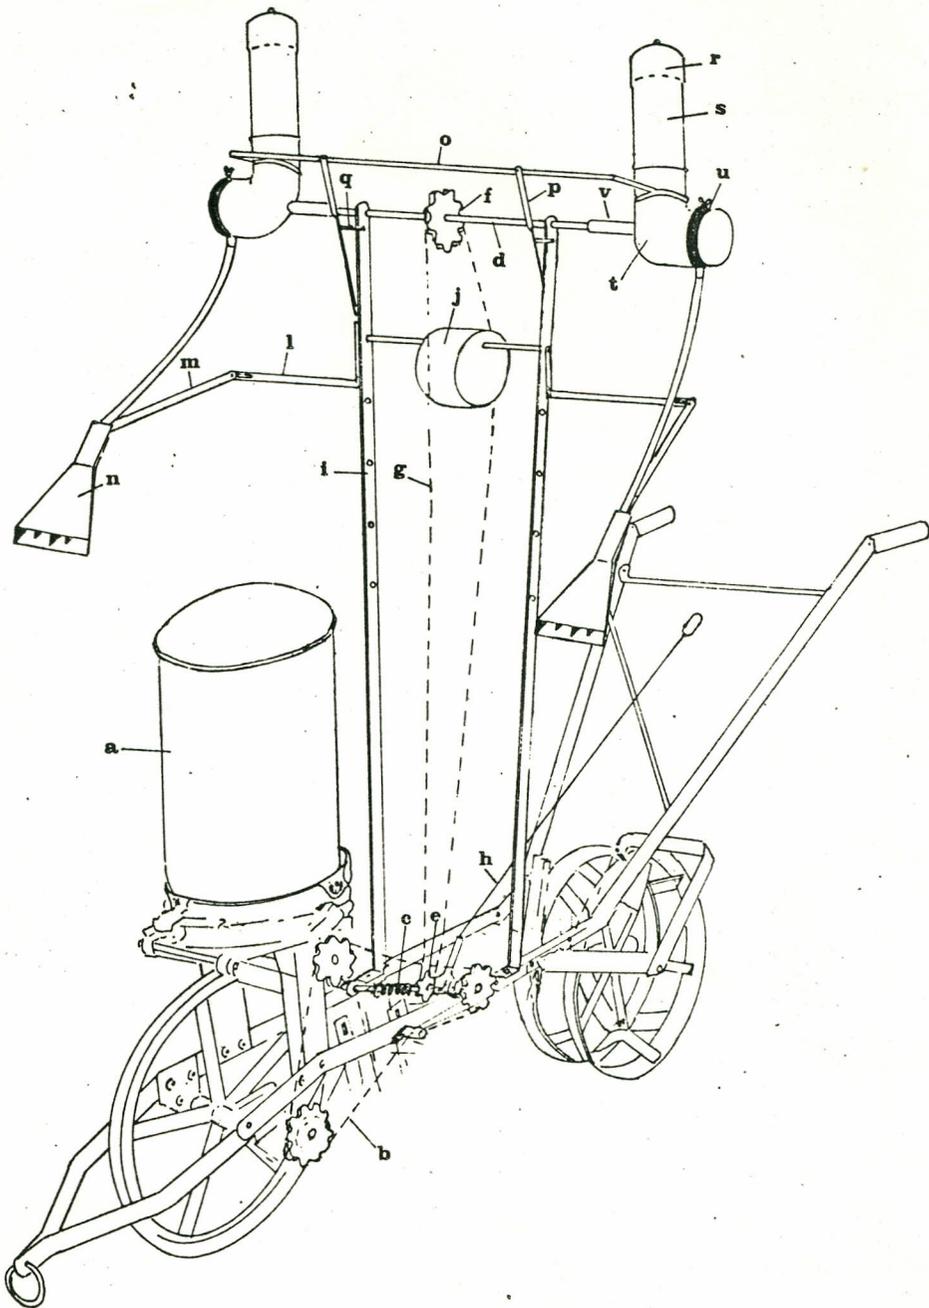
Desenho esquemático do implemento para aplicação de inseticida granulado diretamente no cartucho das plantas de milho ou de sorgo, adaptado à plantadeira de tração animal. (a) - Depósito de adubo; (b-g) - corrente; (c-d) - eixo; (e-f) - engrenagem; (h) - alavanca para acionar o sistema; (i-m-l-o-p) - hastes; (j) esticador; (n) - leque; (q) suporte de haste; (r) - tampa do depósito de inseticida; (s-t) - depósito de inseticida; (u) - regulador de vazão.
